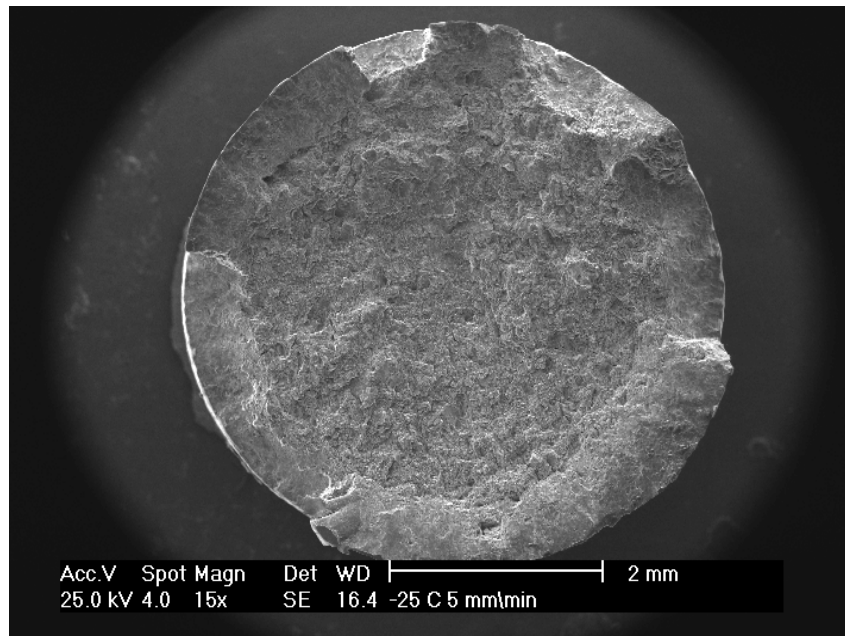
a: Superficie fracturada de la sección transversal de la probeta
